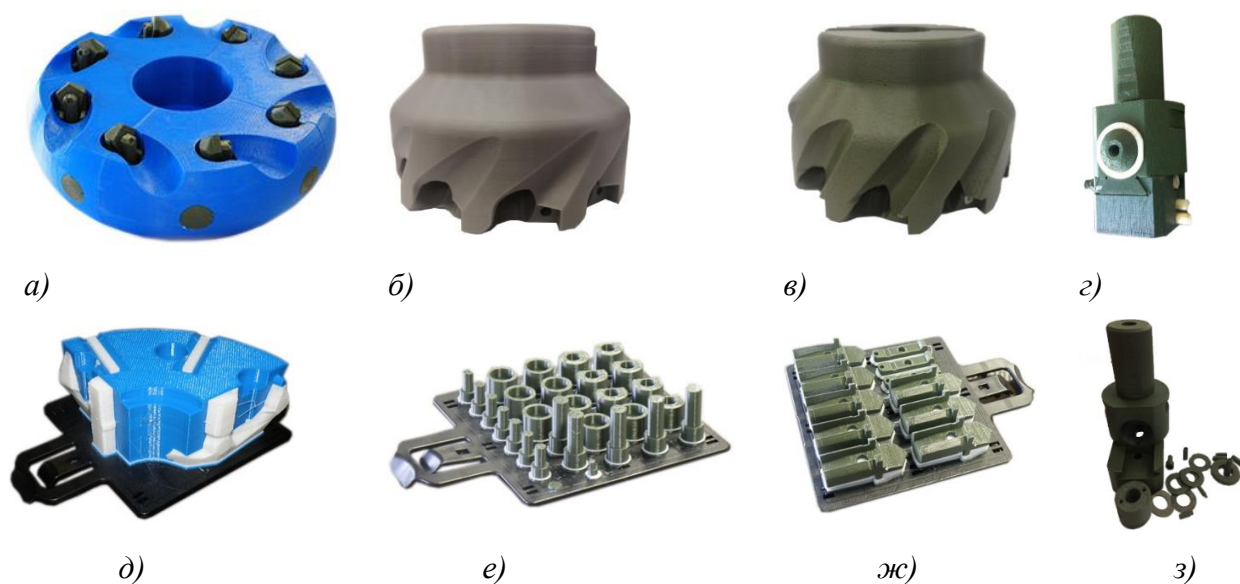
Макеты конструкций блочно-модульных торцовых фрез, расточного патрона и основных элементов, выполненных с применением технологии трёхмерной печати: а –торовая фреза; б и в – цилиндро-конические корпуса фрез; г – цилиндрический корпус расточного патрона; д – сегмент корпуса фрезы; е-з – сухари, винты, корпуса блоков резцовых
